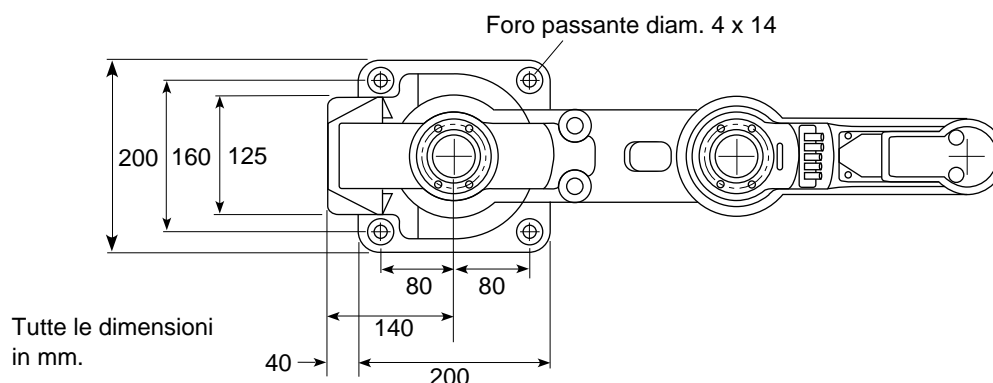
Percorso del foro di montaggio (tra robot e superficie di montaggio)
